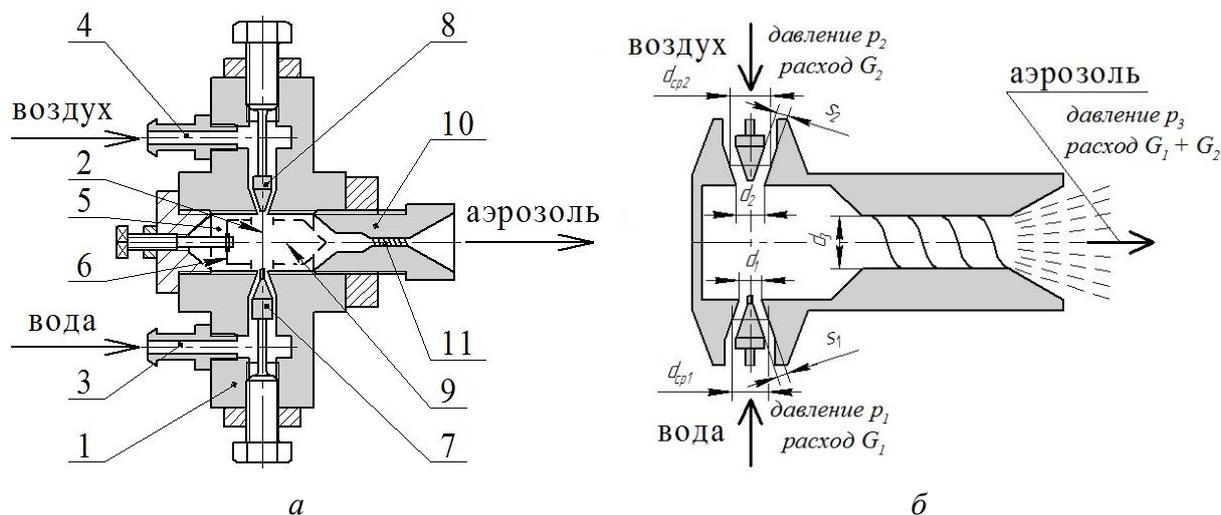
Схемы мелкодисперсного пневмогидравлического увлажнителя: а – конструктивная; б – эквивалентная
